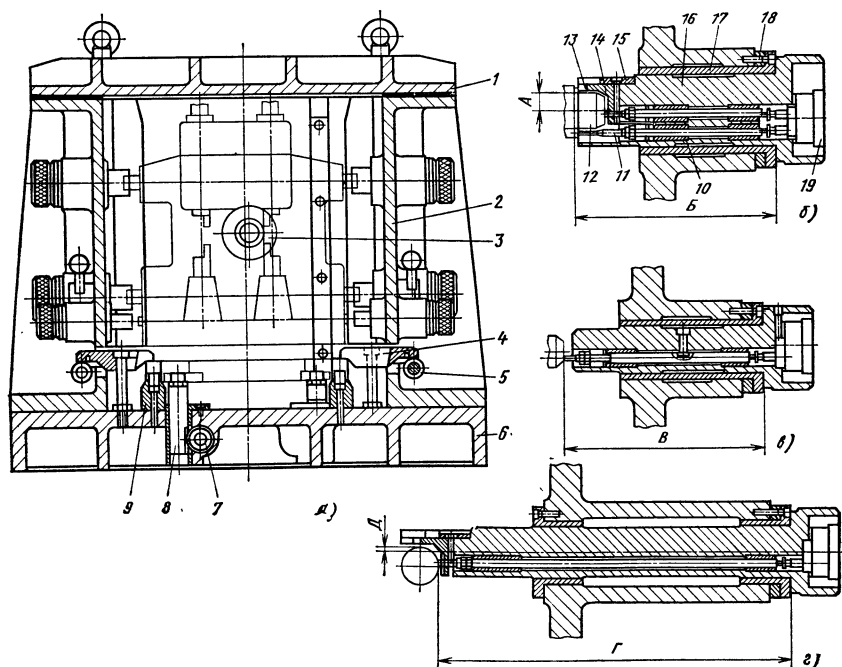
Измерительный стенд для контроля приспособлений-спутников:
